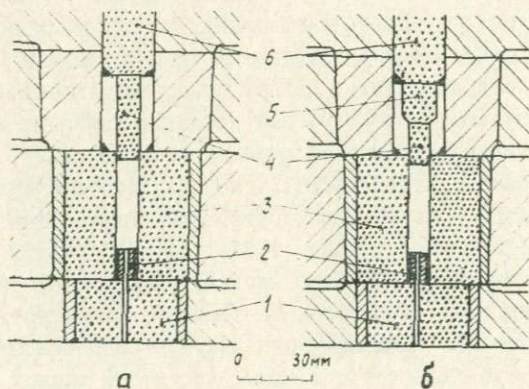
Твердосплавные детали двухступенчатого аппарата. Первоначальный (а) и улучшенный (б) варианты. 1-крышка цилиндра, 2-электроввод, 3-цилиндр, 4-рабочий шток, 5-пята, 6-промежуточный шток.
